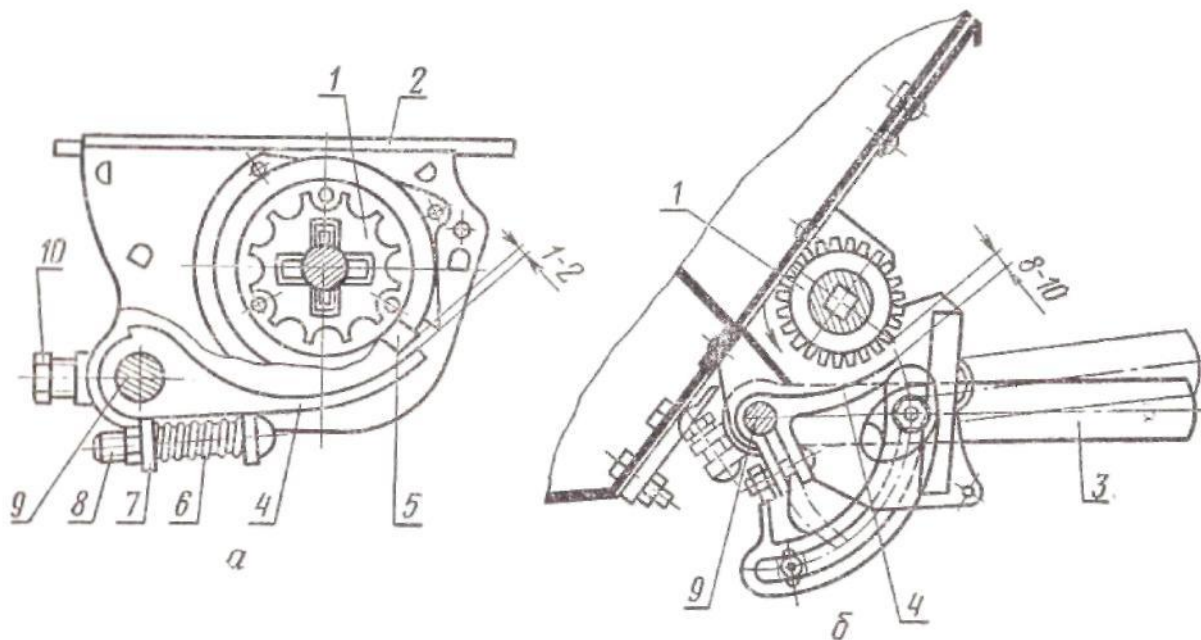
Высевные аппараты зерновой сеялки СЗ-3,6: а – аппарат для семян; б – аппарат для посева гранулированных удобрений; 1 – катушка; 2 – коробка; 3 – рычаг вала клапанов; 4 – клапан; 5 – ребро муфты; 6 – пружина клапана; 7 – вставка клапана; 8 – болт; 9 – вал клапана; 10 – стопор
